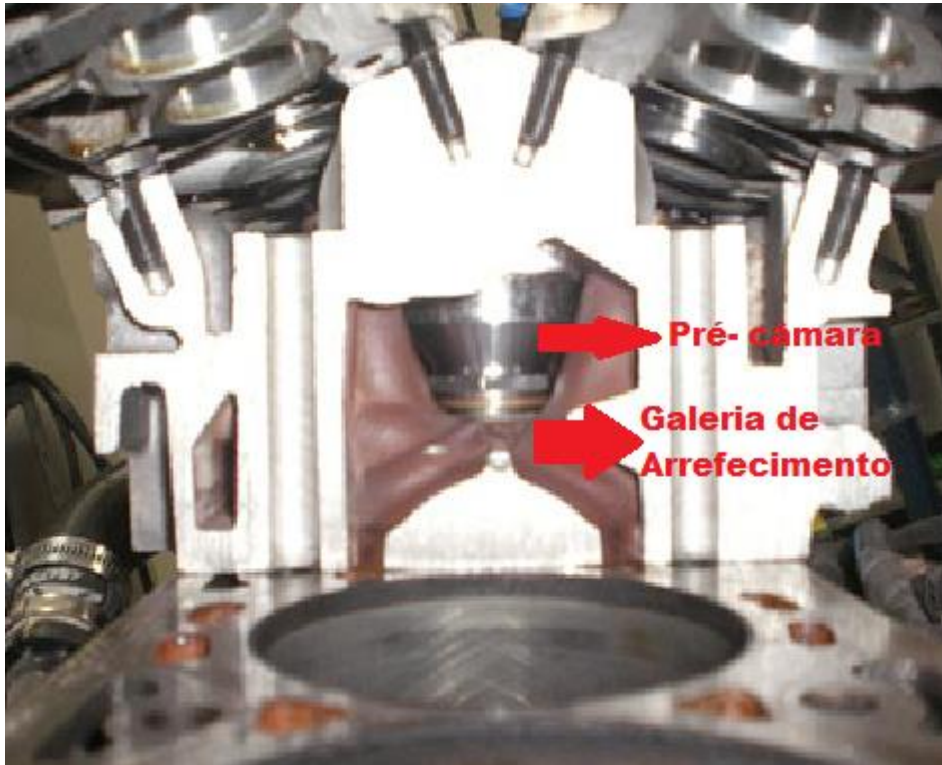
Galeria de arrefecimento do motor para arrefecimento da pré-câmara instalada.
